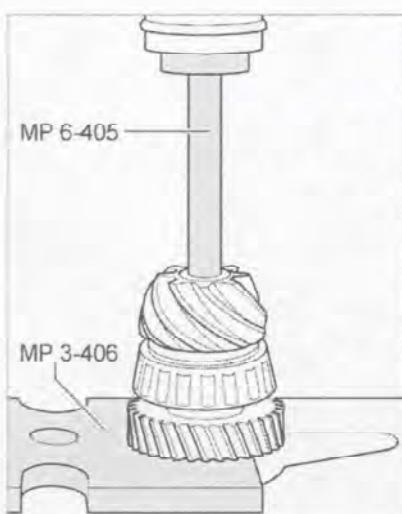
Напрессуйте шестерню 4-й передачи на вал с помощью специального инструмента.
